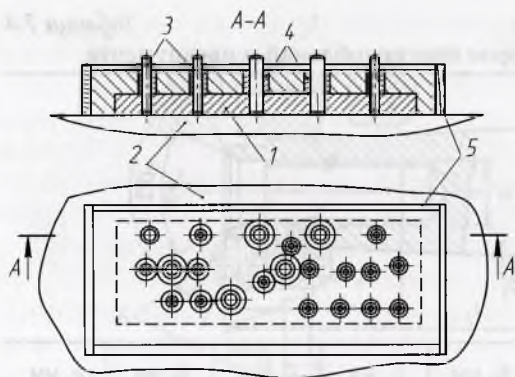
Изготовление корпуса сверлильного приспособления (кондуктора) литьем из компаунда на базе эпоксидно-диановых смол
